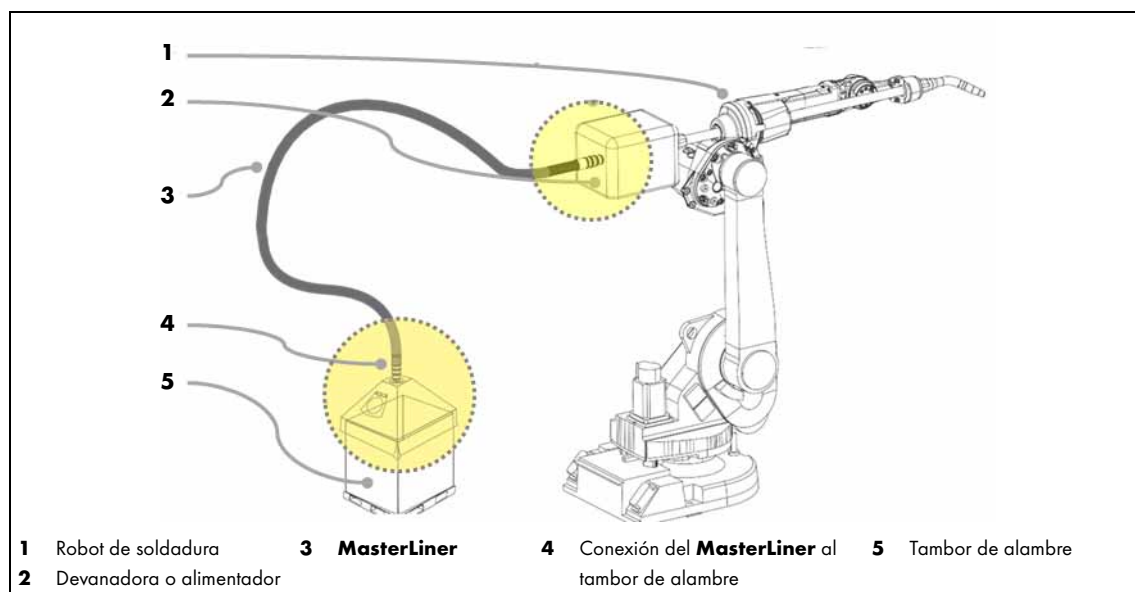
Tendido de la célula de soldadura robotizada
